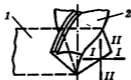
Совмещение проекций режущей части сверла и резца:
